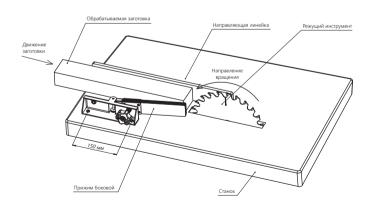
Б Установка прижима бокового на станок с вращением инструмента против часовой стрелке
